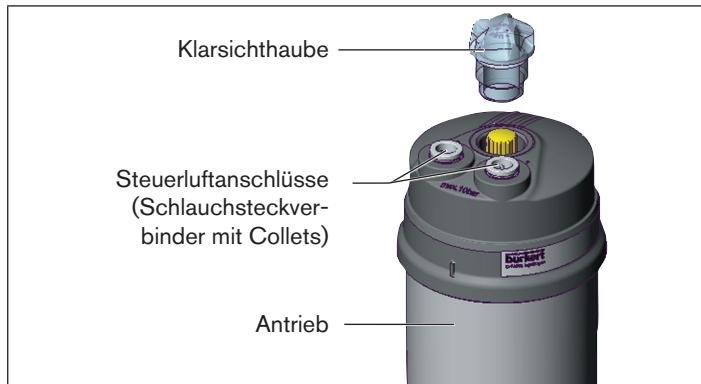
Montage der Schaltspindel (1), Reihe 21xx
